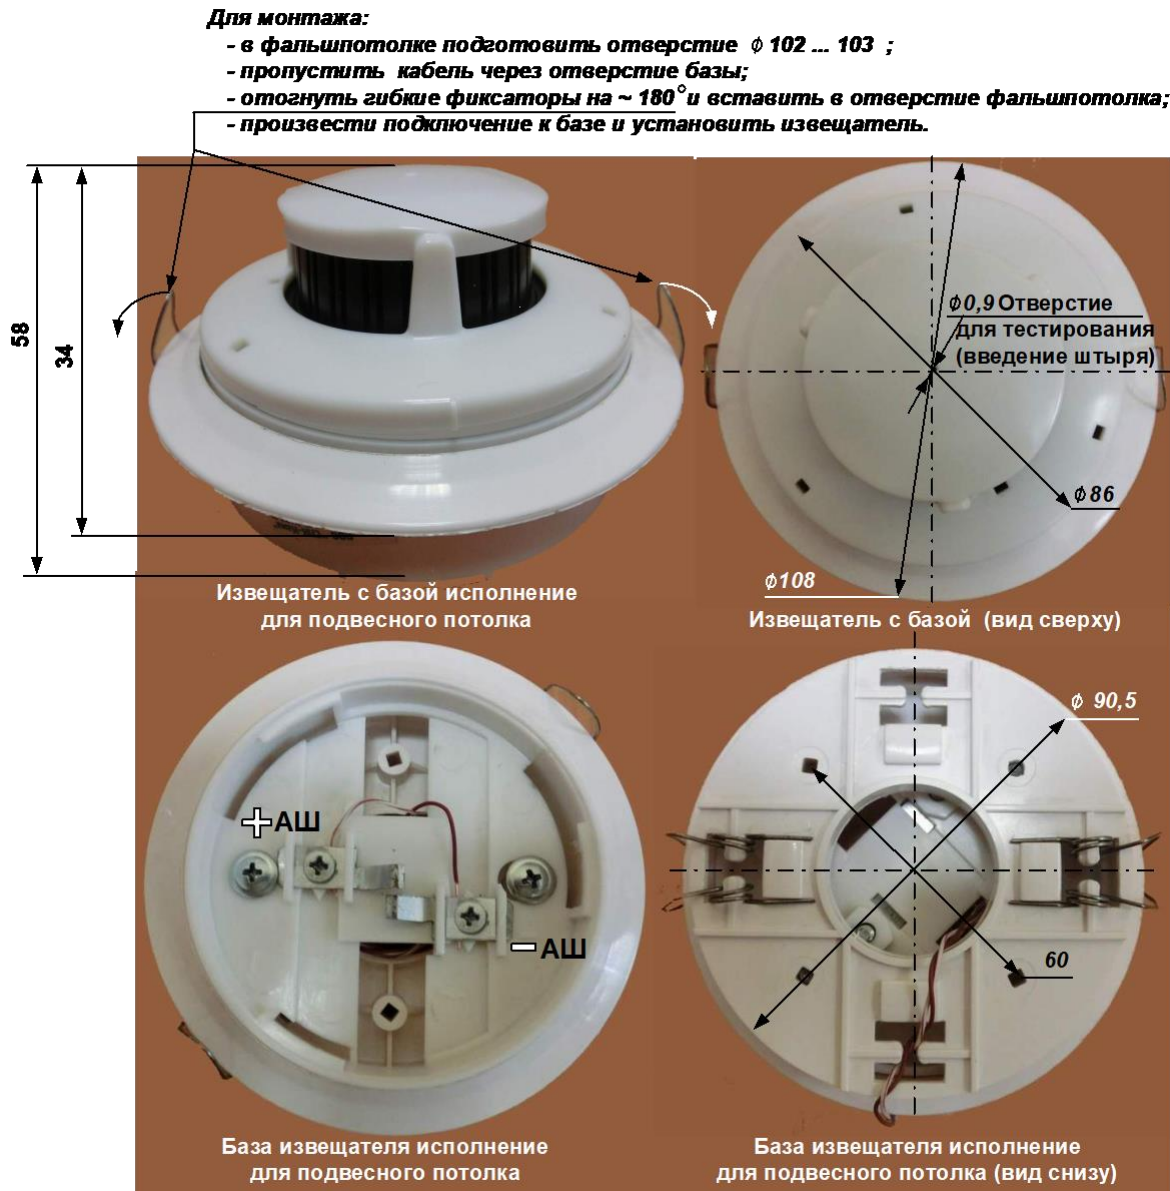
АТИ (блок извещателя, база). Габаритные и присоединительные размеры.
